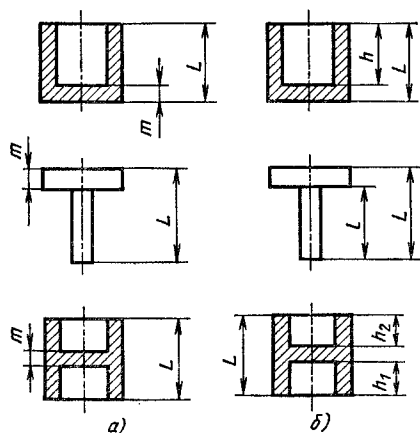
Примеры базирования и простановки размеров заготовок, полученных выдавливанием:  $m$  — толщина дна;  $L$  — длина (высота) заготовки;  $h_1$  и  $h_2$  — глубина полости
